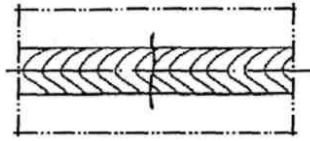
10. Поперечная трещина сварного соединения
